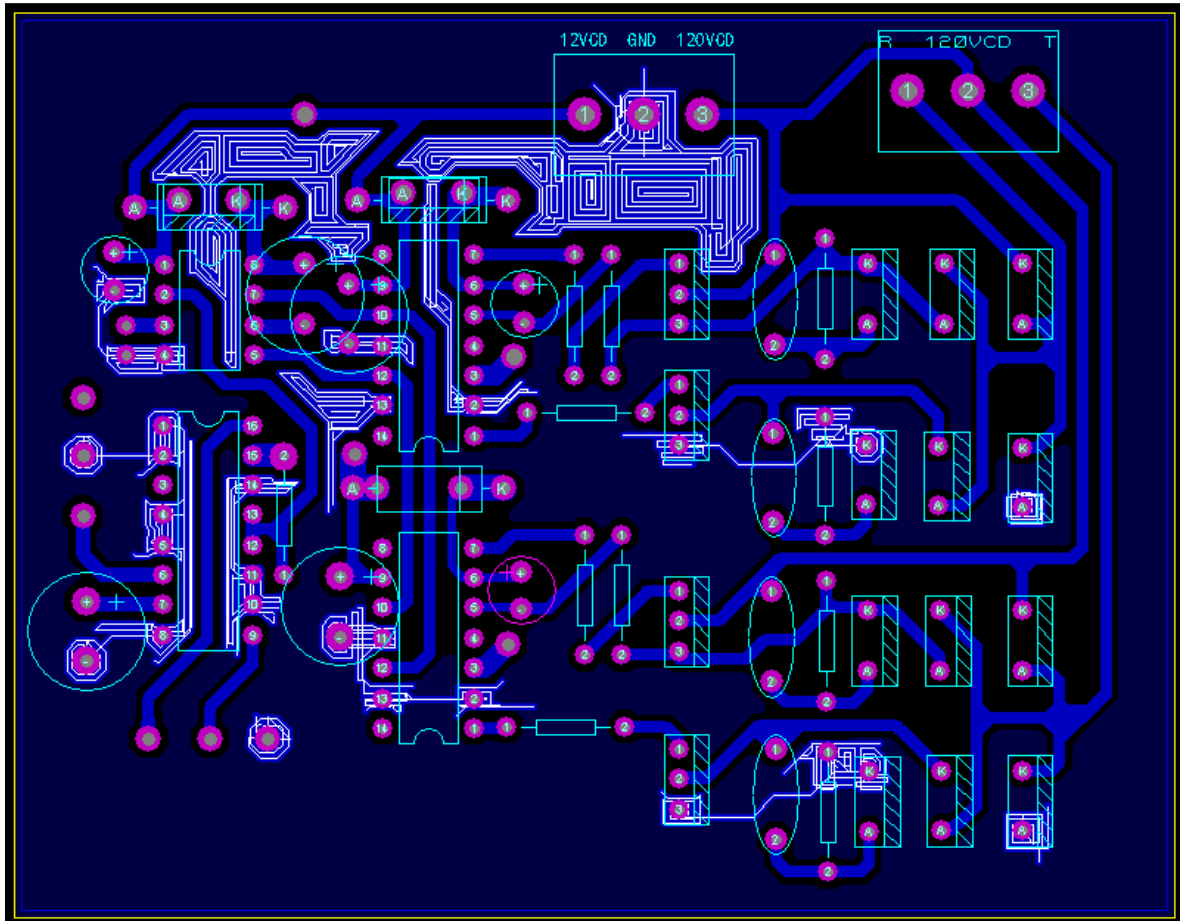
PCB del inversor monofásico y la etapa de control.
